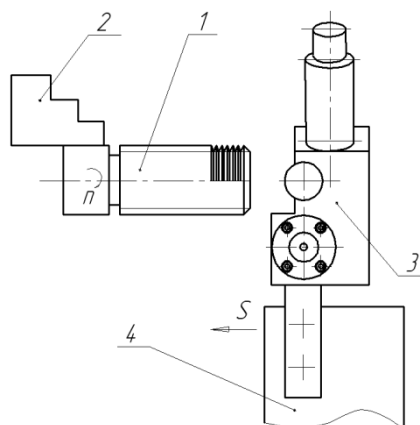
Схема розташування пристрою для нанесення на різьбову поверхню легкоплавкого сплаву на токарному верстаті: 1 – виріб; 2 – патрон; 3 – система подачі пасти; 4 – супорт токарного верстата
